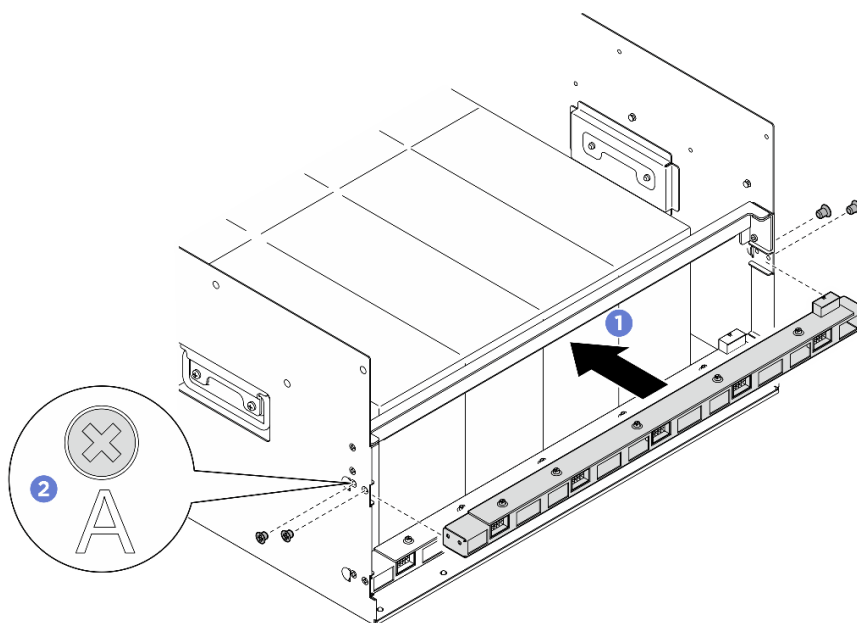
Installation der hinteren Lüfterplattenbaugruppe
